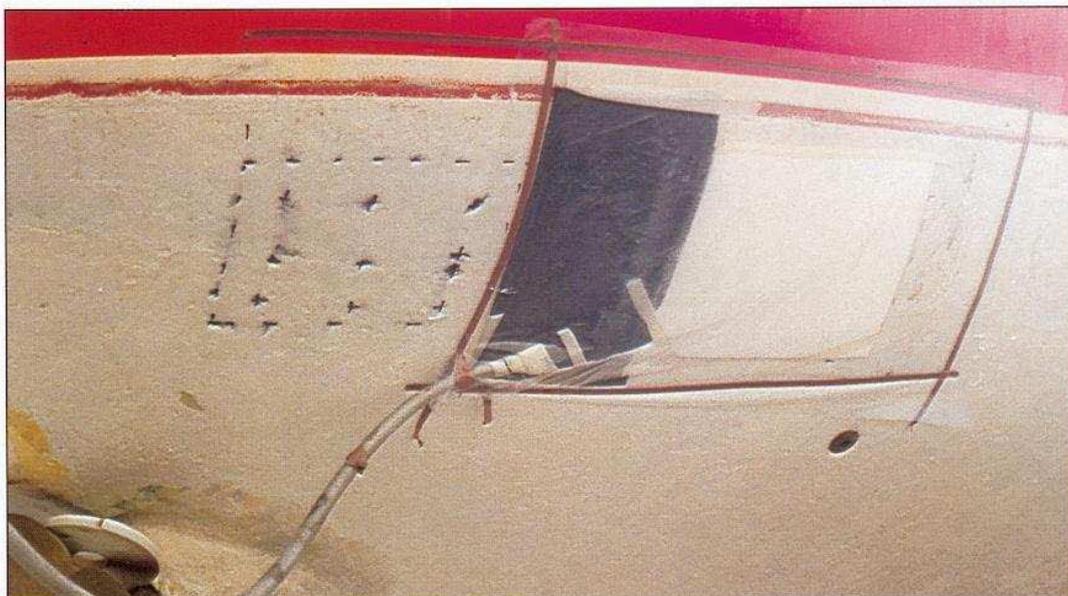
extraction par le vide : tissu de pompage et joint d'étanchéité adhésif double-face
